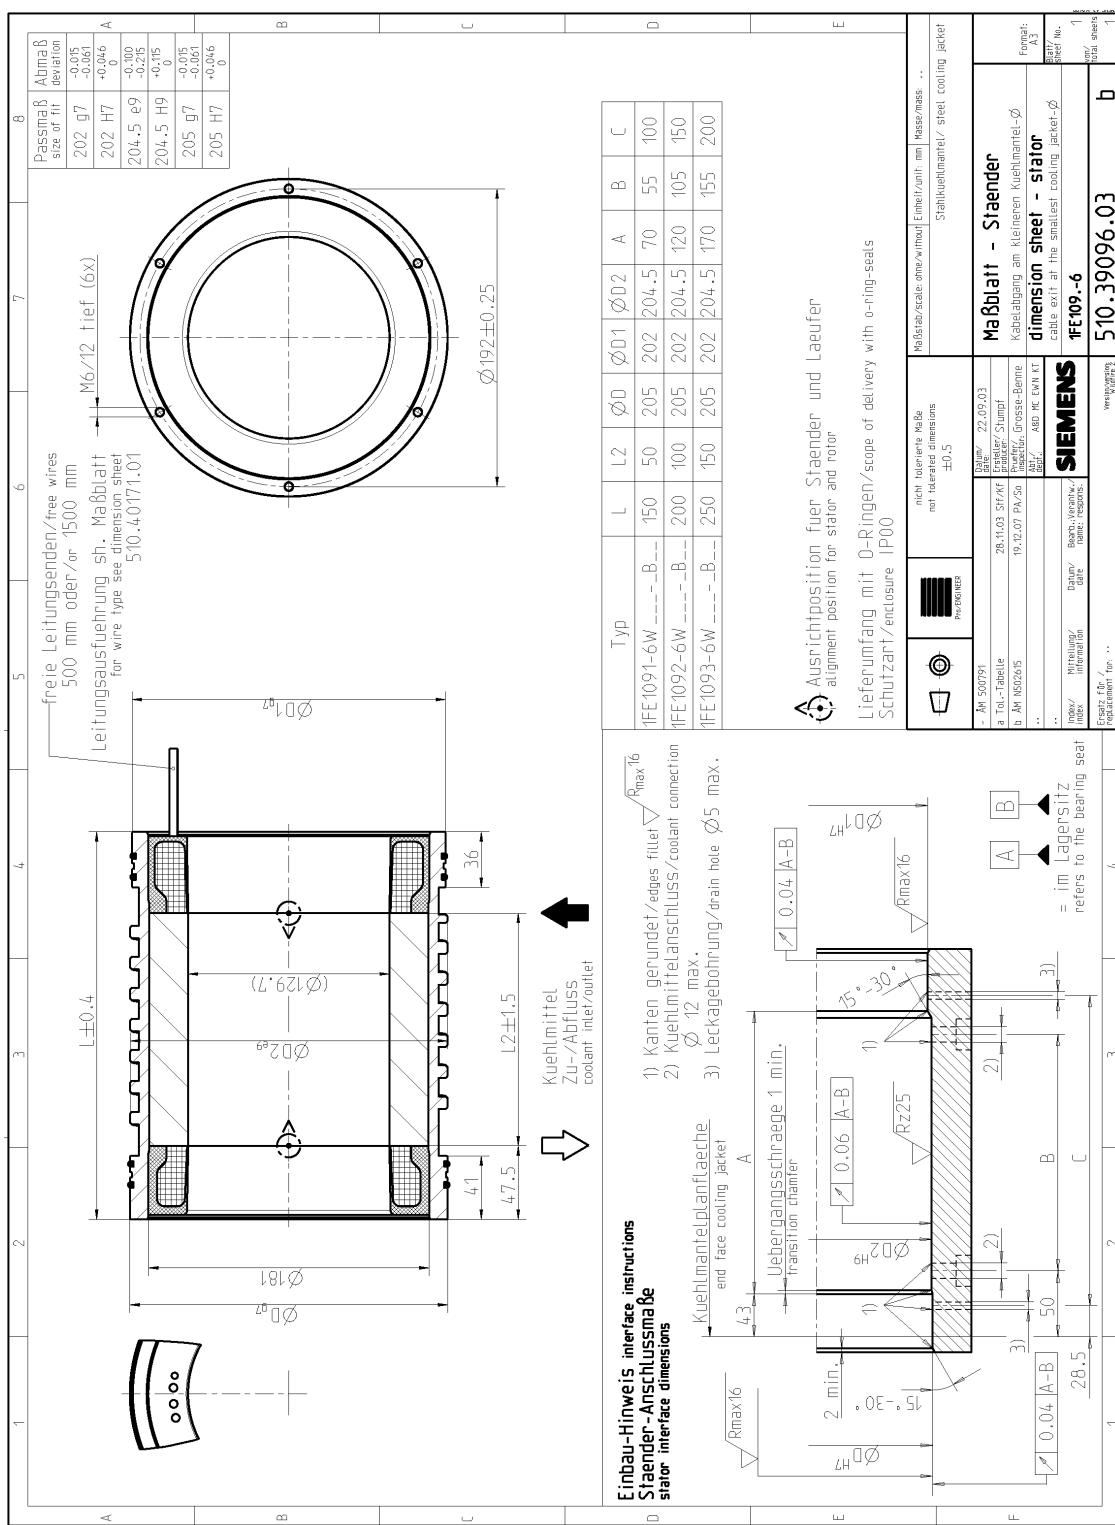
1FE109□-6, Ständer mit Kühlmantel, Kabelabgang am kleineren Kühlmanteldurchmesser
